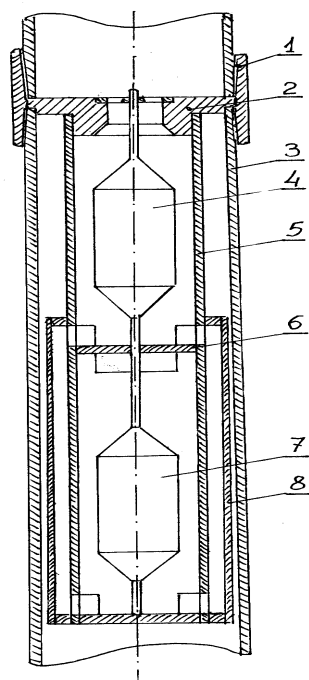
Запорное устройство АЗЗУ-2П: 1 – муфта; 2 – седло; 3 – обсадная колонна; 4 – верхний поплавок; 5 – корпус; 6 – перегородка; 7 – нижний поплавок; 8 – обтекатель
